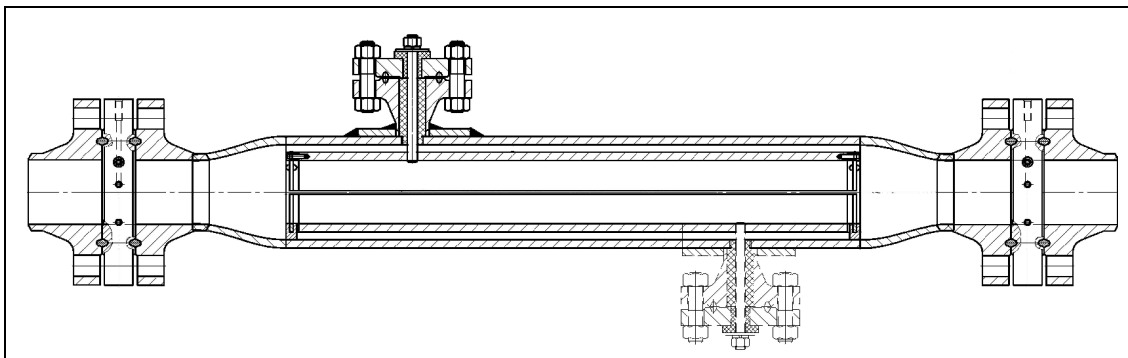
Сборочный чертеж конструкции измерительного участка
